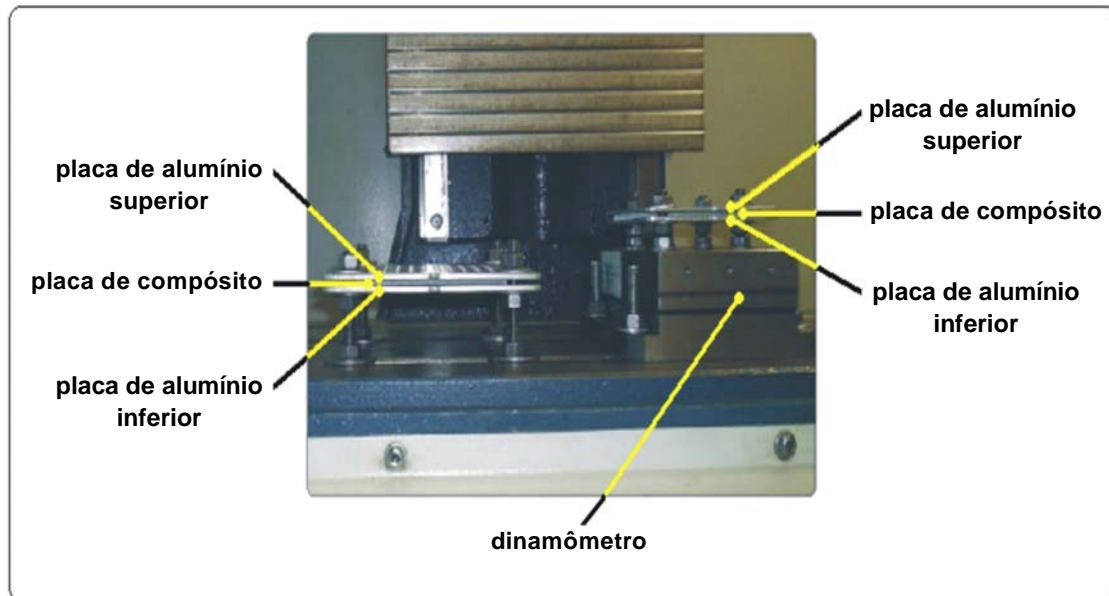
Detalhe da montagem utilizada para a furação dos corpos-de-prova.
